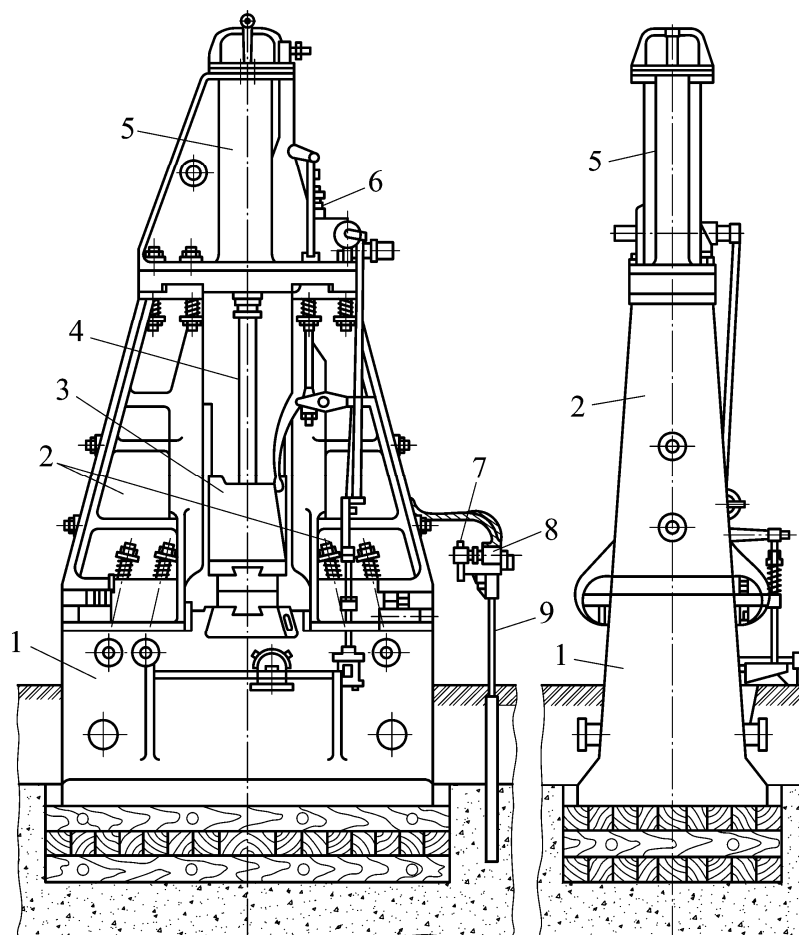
Паровоздушный штамповочный молот: 1 – шабот; 2 – стойки станины; 3 – баба; 4 – шток; 5 – рабочий цилиндр; 6 – золотниковая коробка; 7–9 – устройства для смазки узлов 5, 6
